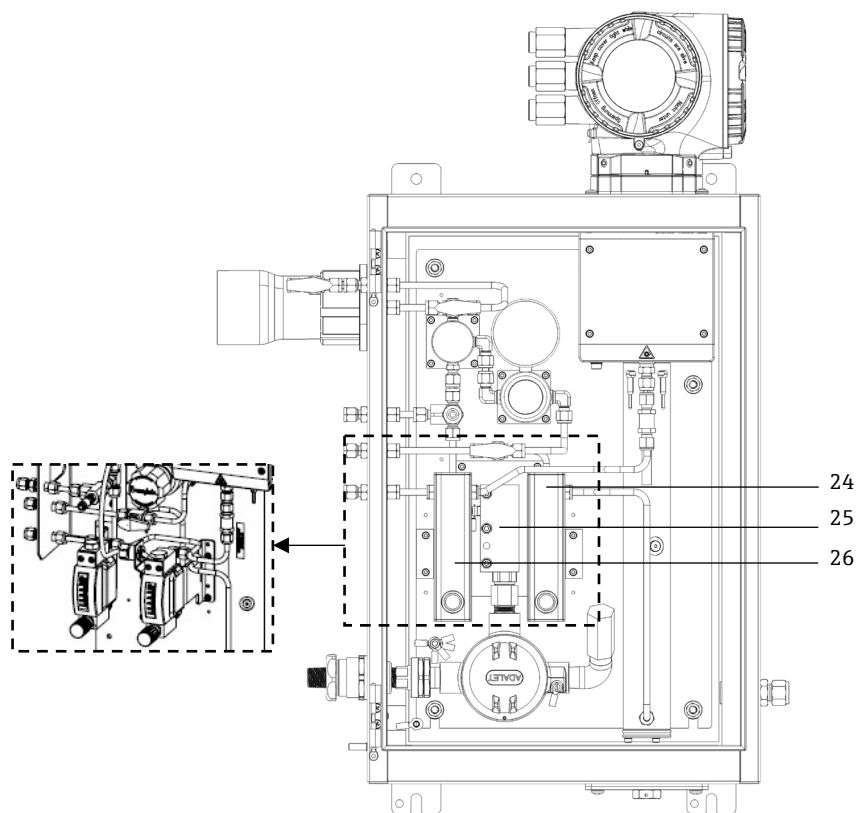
Запасные части для анализатора J22 с системой подготовки проб в корпусе
